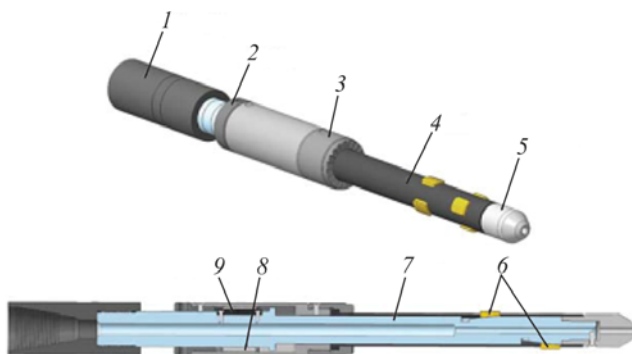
Общий вид труболовки внутренней: 1 – переводник; 2 – втулка; 3 – втулка фрикционная; 4 – кожух; 5 – наконечник; 6 – плашка; 7 – корпус; 8 – втулка резьбовая; 9 – шпонка
